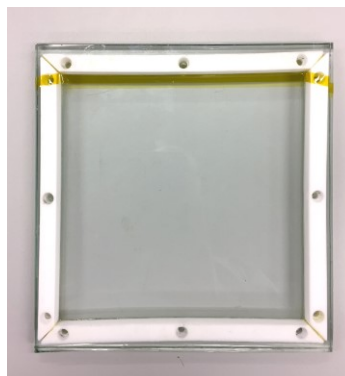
Molde utilizado para a fabricação dos filmes finos de PVA
